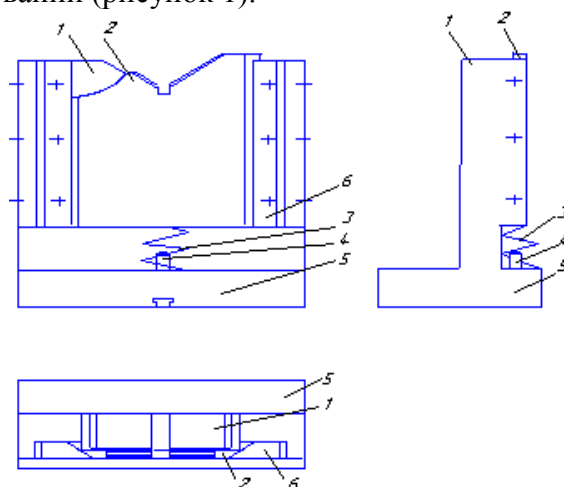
Опора для правки и контроля прогиба валов: 1-призма правильная; 2-призма контрольная подвижная; 3-пружина; 4-стержень направляющий; 5-основание опоры.
